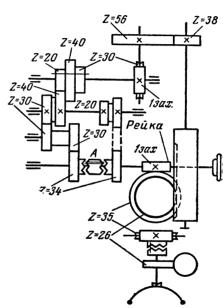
Кинематическая схема механизма подач шпинделя станка модели 2A420
